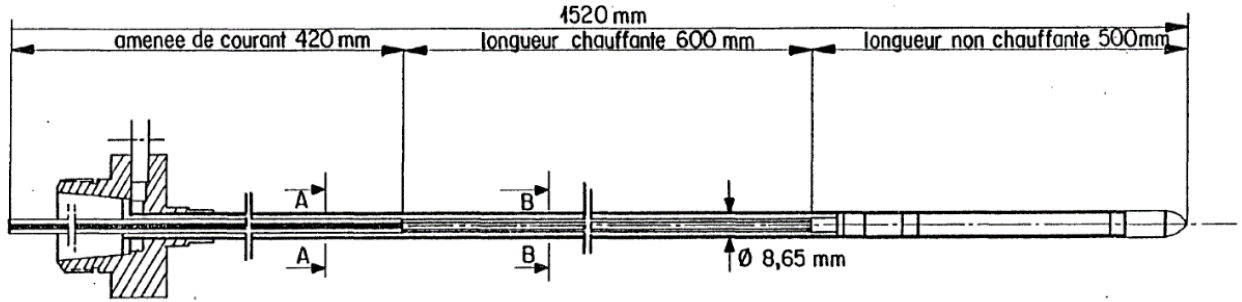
Coupe verticale de l'aiguille chauffante de la section d'essai de la boucle CESAR. [16]
